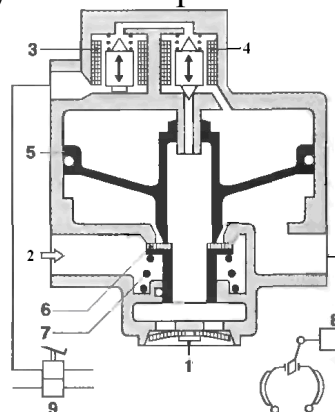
Трифазний релейний МТ на базі КПД фірми Bosch [6]: 1 – випуск в атмосферу; 2 – подача повітря; 3 – клапан підтримки тиску; 4 – клапан зменшення тиску; 5 – поршень, що управляє; 6 – клапан; 7 – пружина; 8 – ГК; 9 – пневматичний гальмівний кран.
